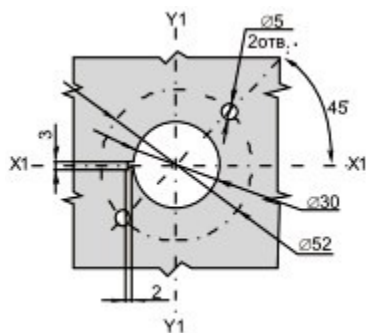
Шаблон для сверления отверстий в двери для установки привода ПРП-32
